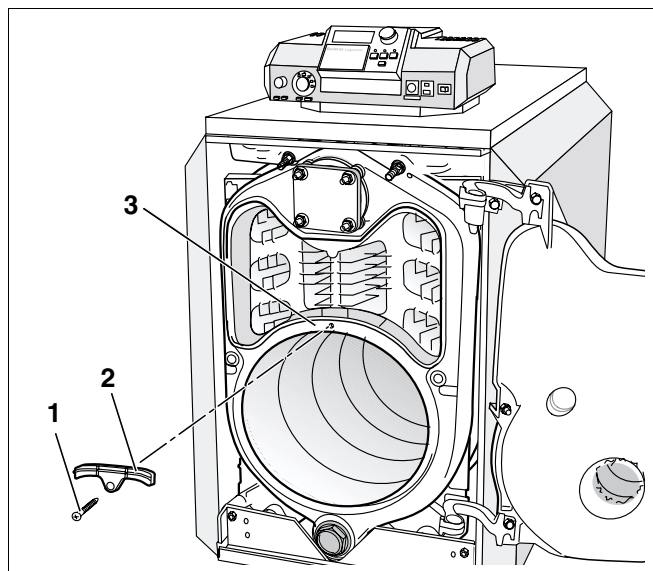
Se îndepărtează placa de blocare pentru gaze
